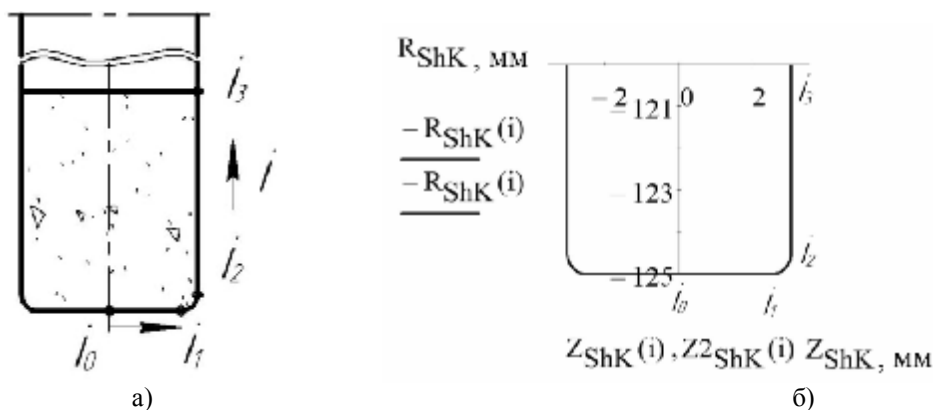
Профіль шліфувального круга для обробки циліндричних деталей
